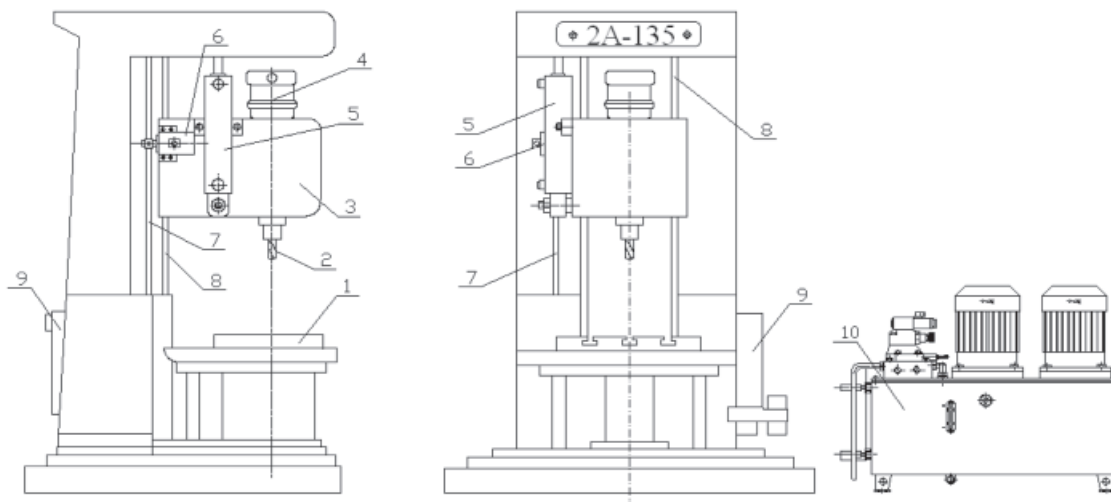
Общий вид координатно-сверлильного полуавтомата:
